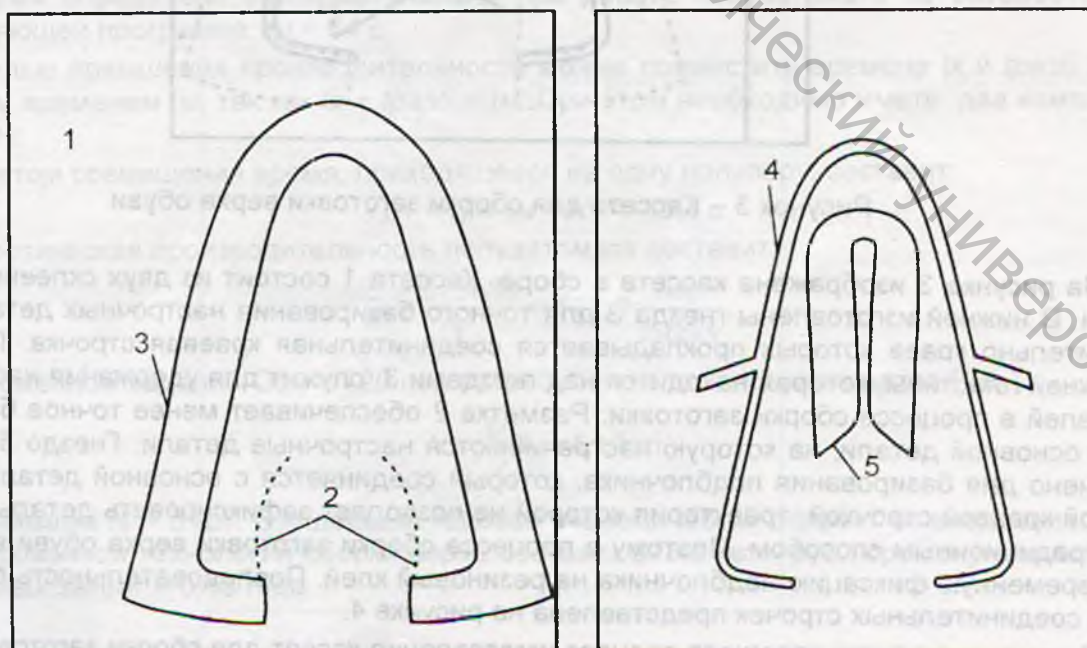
Пластины кассеты для сборки заготовки на полуавтомате
